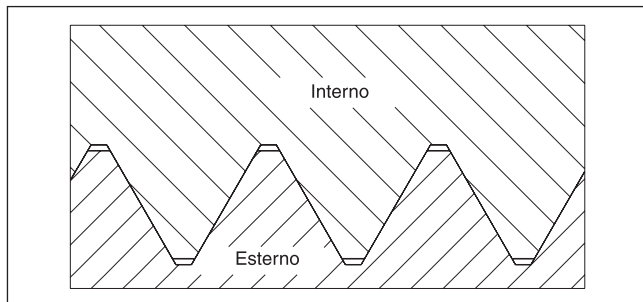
NPT – Serraggio a chiave – Nessun contatto cresta-fondo – Solo i fianchi a contatto.
